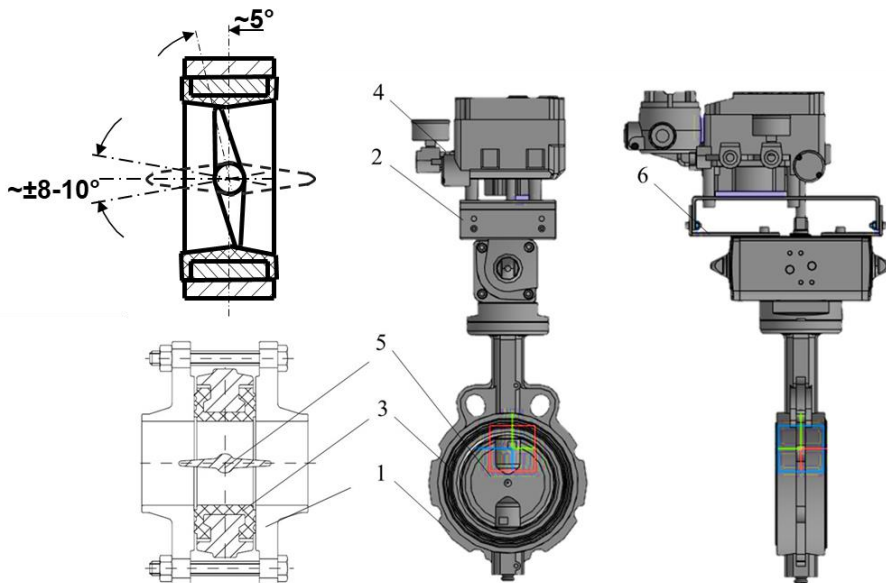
Дослідна модель ЗРП: 1 — корпус; 2 — поворотний пневматичний привод; 3 — ущільнення; 4 — електропневматичний позиційний привод; 5 — диск; 6 — монтажна платформа
